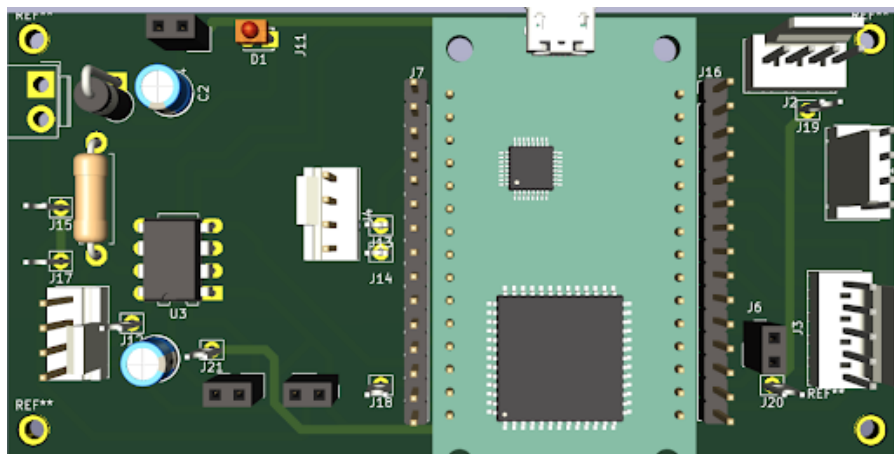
Vista tridimensional de la placa de control ensamblada.
